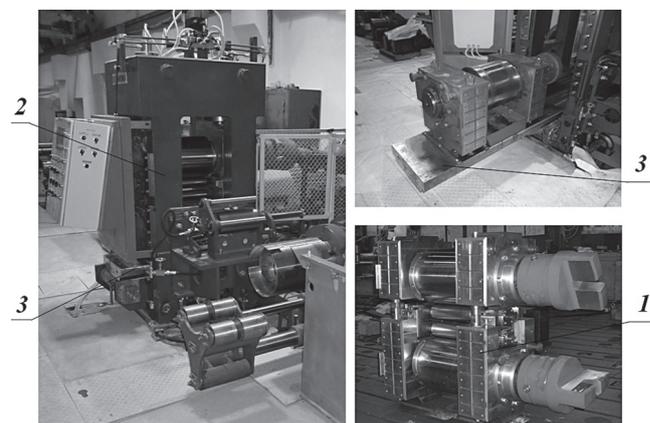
Рабочая клетя стана дуо-кварто 320хп: 1 – валковая кассета кварто; 2 – станина; 3 – перевалочная плита
